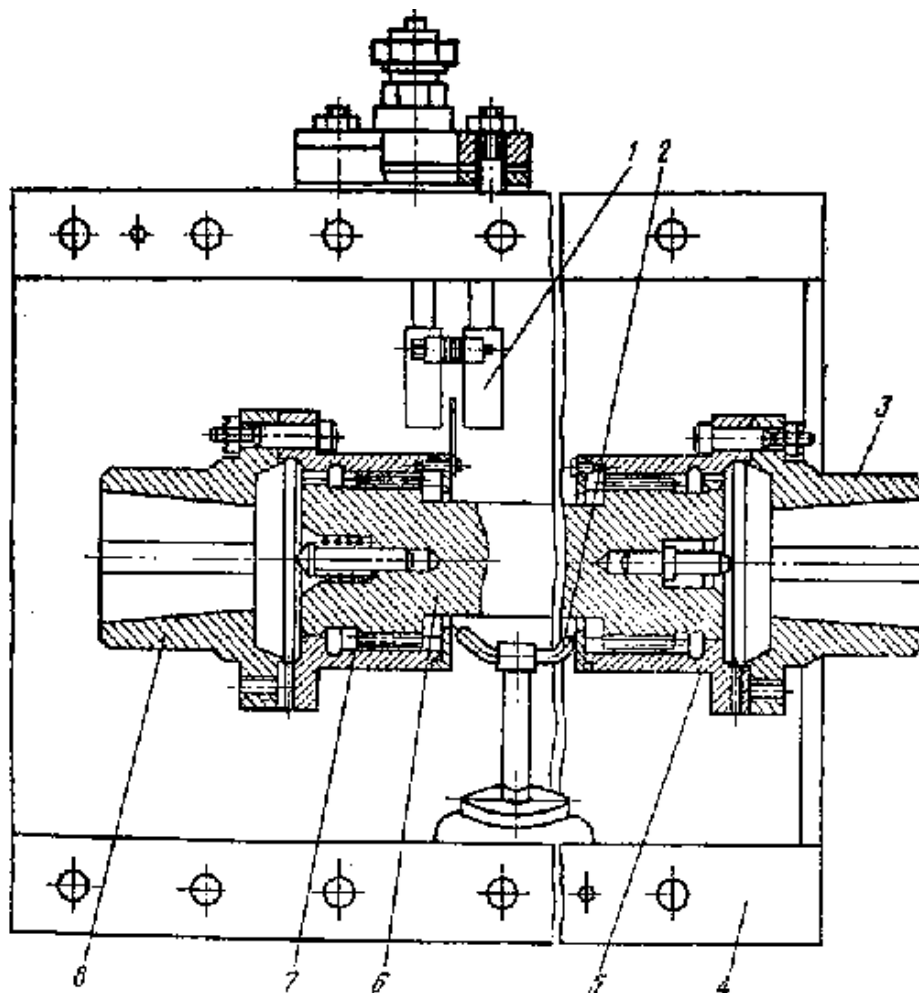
Зубчатая муфта «мультипликатор – компрессор»
